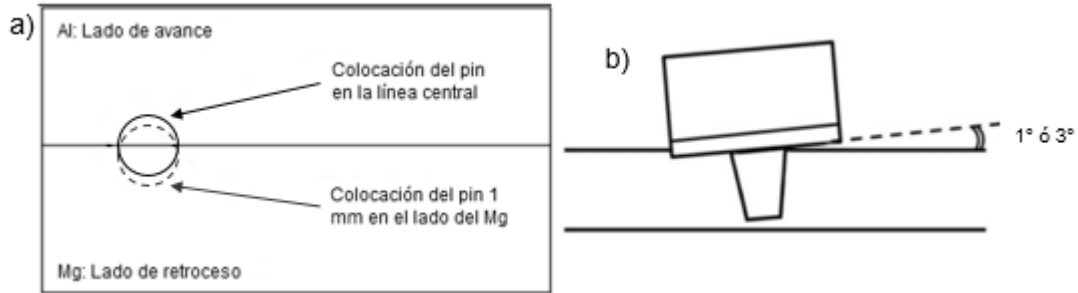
a) Colocación del pin 1 mm en el lado del magnesio (Offset), b) Ángulo de inclinación entre la superficie de la soldadura y la herramienta de FSW.
